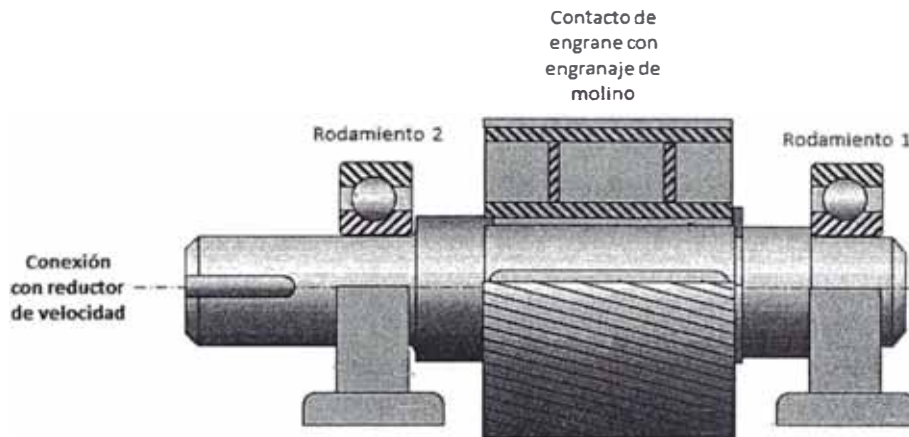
Instalación del piñón. Dos rodamientos de apoyo, un contacto de engrane con engranaje de molino
